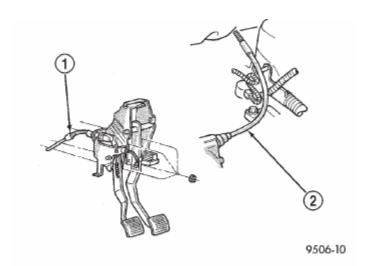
Encaminado del cable de embrague 1 – CABLE DE EMBRAGUE EN EL PEDAL DE EMBRAGUE
